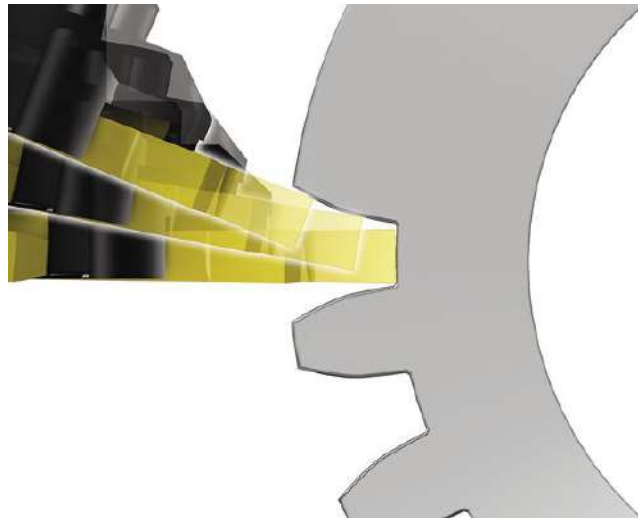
Фрезерування верхньої частини профілю зубу [7]
